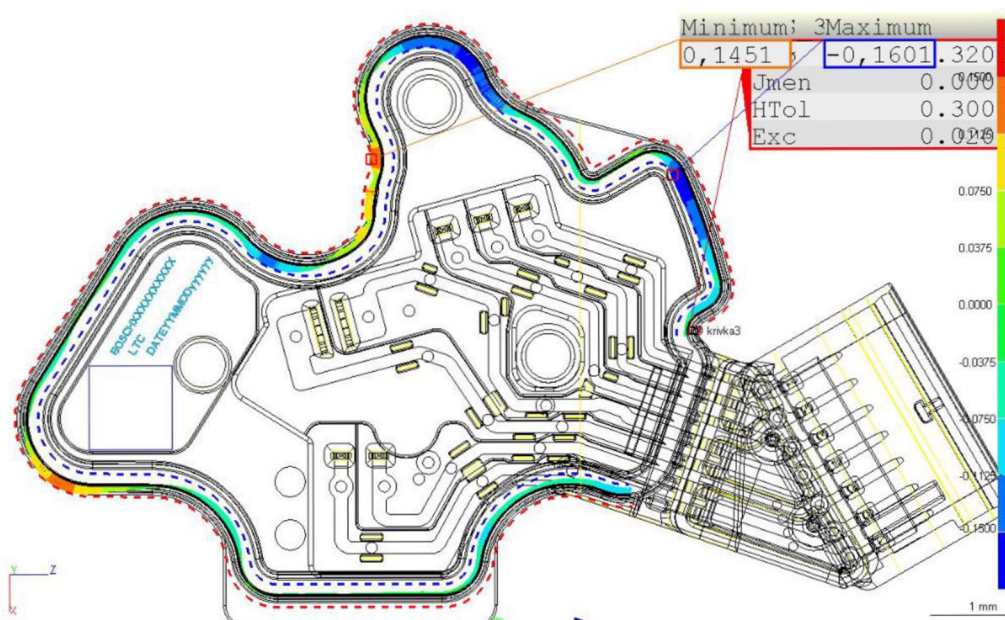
Vybrání hrany vodící podložky Obr. 91 Vybrání a tvaru pojistného kolíčku
